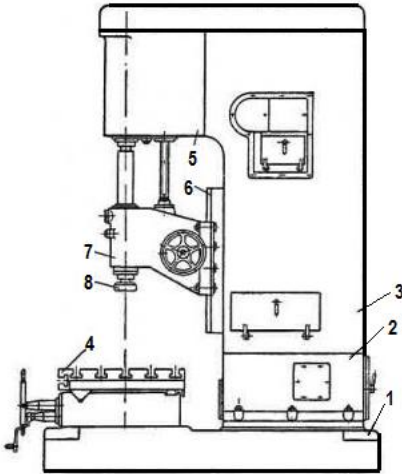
Вертикальний алмазно-розточувальний верстат
